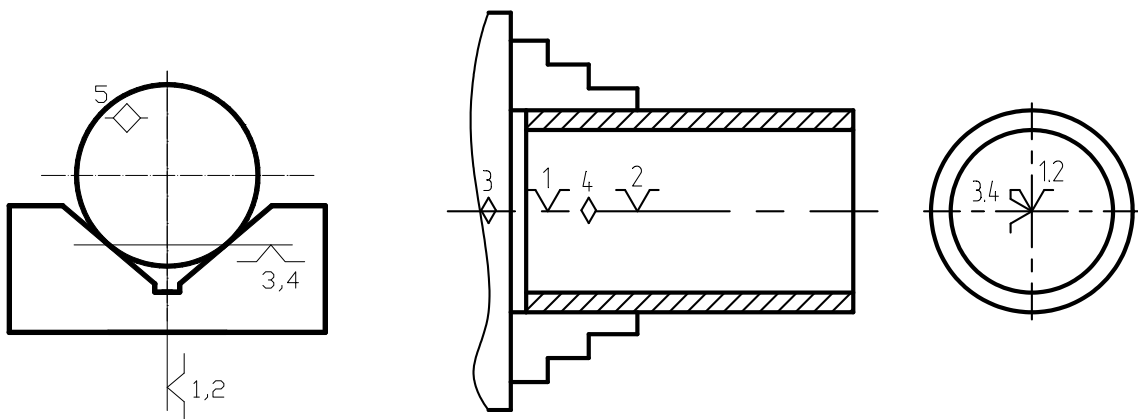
Базування втулок за чистовими базами (в призмi) при свердлінні поперечних отворів, фрезеруванні тощо
